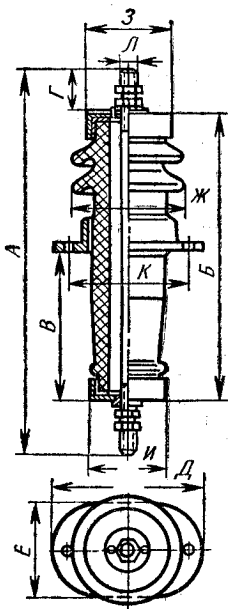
Проходные изоляторы для наружной установки ПНБ-6/400, ПНБ-6/600, ПНБ-6/1000, ПНБ-6/1500.
